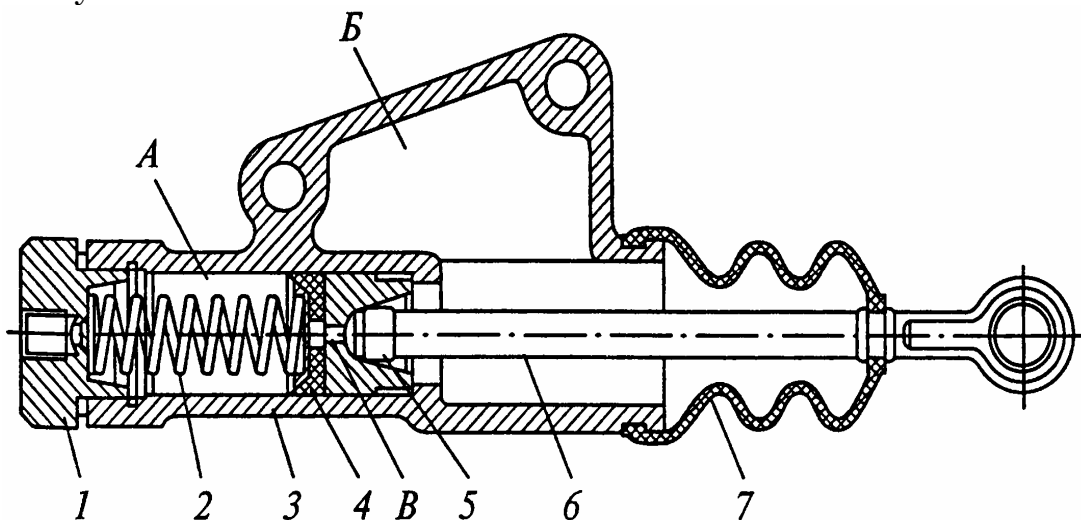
Главный цилиндр привода сцепления грузовых автомобилей КамАЗ: 1 – пробка; 2 – пружина; 3 – корпус; 4 – манжета; 5 – поршень; 6 – шток; 7 – чехол; А, Б – полости; В – отверстие
